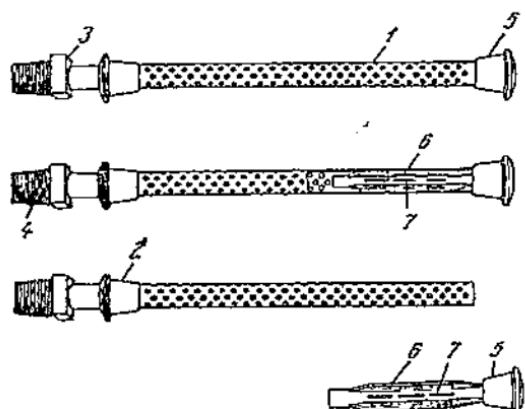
Схема обыкновенного цилиндрического шпинделя для крестовых шпуль.
